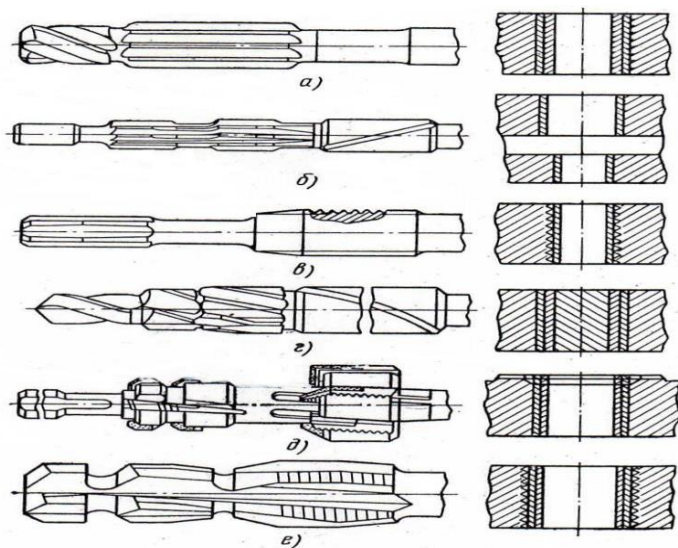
Конструкции комбинированных режущих инструментов и схемы их работы: а - зенкер-развертка, б - развертка-развертка, в - развертка-метчик, г - сверло-зенкер-развертка, д - многоступенчатый зенкер, е - зенкер-развертка-метчик
